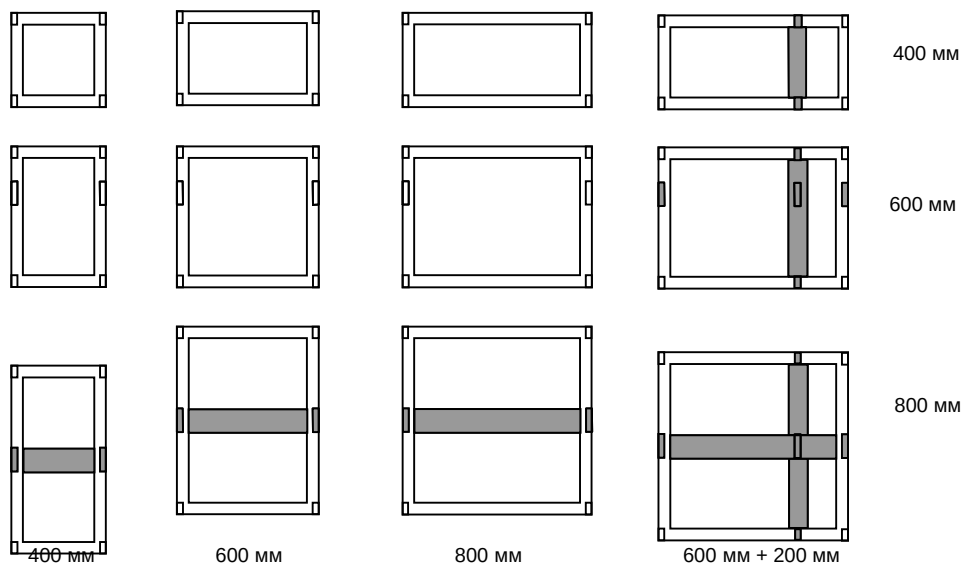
Каркас с внутренними перегородками (вид сверху)
